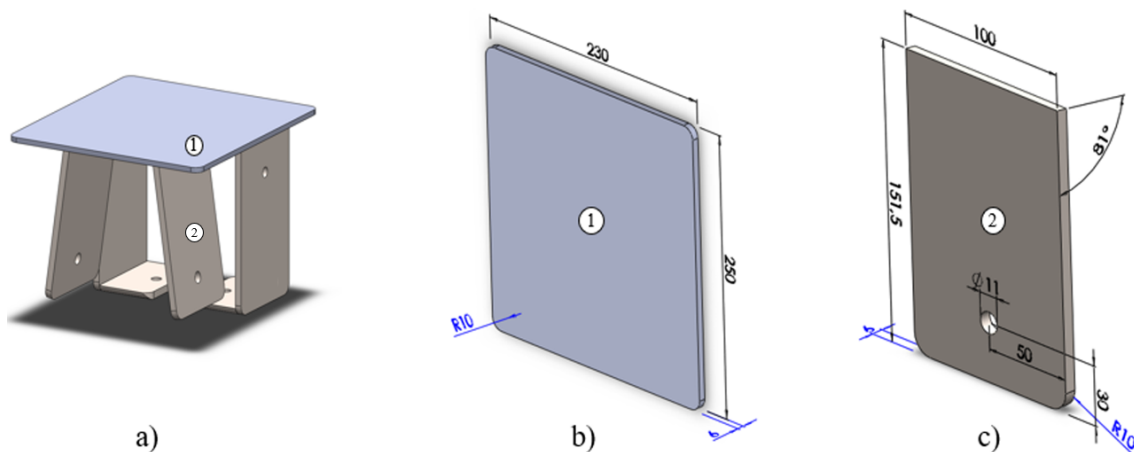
a) Subconjunto em perspetiva; b) Dimensões da Chapa Topo; c) Dimensões da Chapa Oblíqua (mm).
